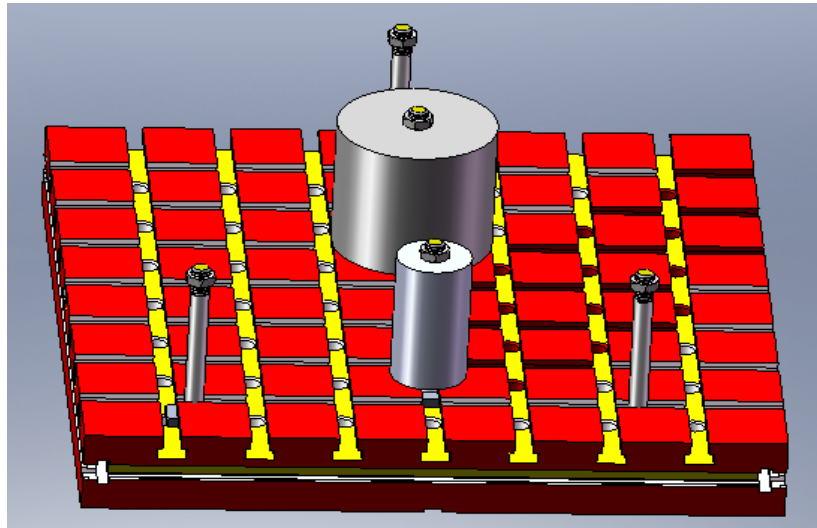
Зовнішній вигляд плити, на яку встановлюється заготовка
